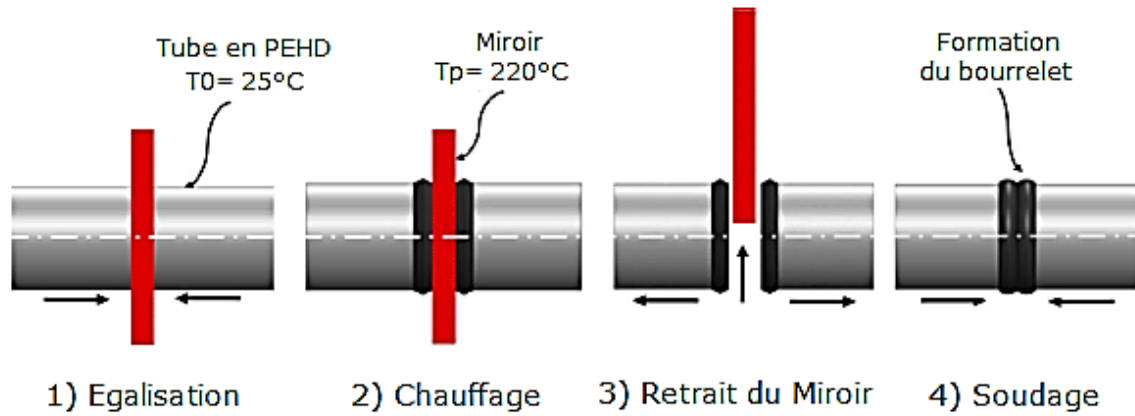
Les étapes de soudage par fusion bout à bout.
